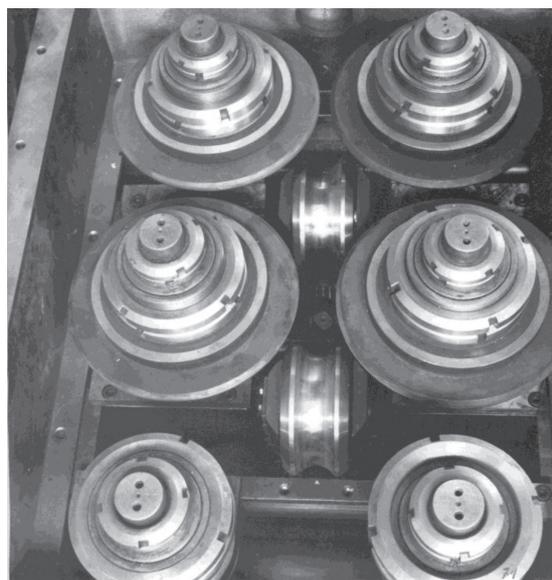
Внешний вид опорно-сварочного узла ТЭСА АДС
